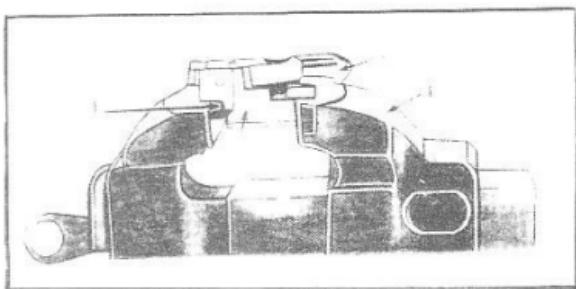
Pribor za vadjenje opruge cevi iz sanduka:
